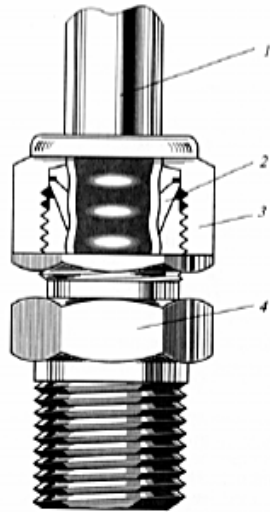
Беспрокладочное нипельное соединение типа «Шваглок»: 1 – трубопровод; 2 – ниппель; 3 – накидная гайка; 4 – штуцер
